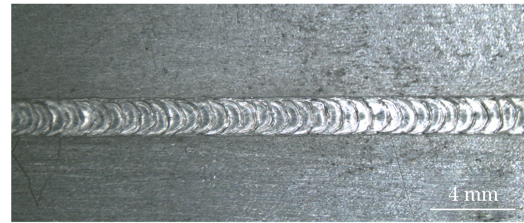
450 °C 热场条件下硼钢/Q235 钢激光焊缝表面形貌
